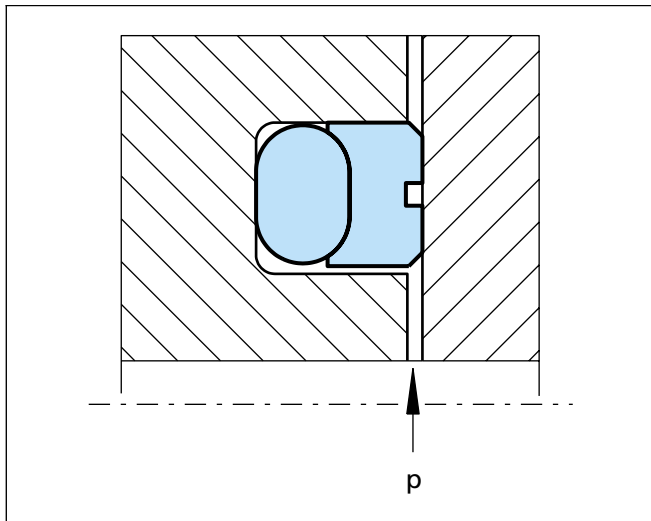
Axialwirkender Turcon® Roto Glyd Ring®
